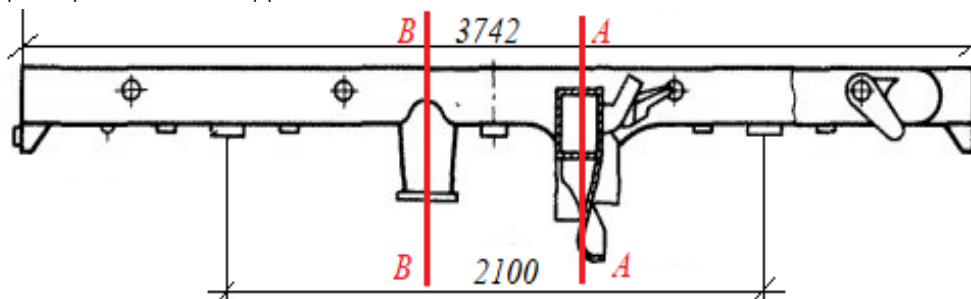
Усиление сечений рамы тележки вагона метрополитена в местах примыкания поперечных балок к продольным (С-С и В-В), а
